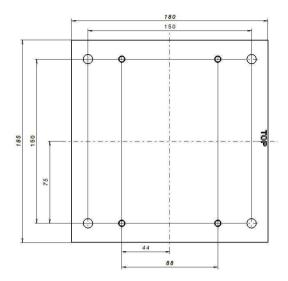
Bohrbild Standard-Wand- Adapterplatte BG D
